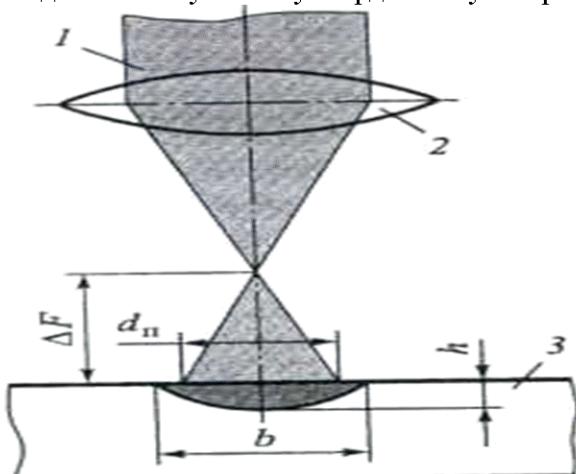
Схема лазерної обробки. 1 – промінь лазера; 2 – лінза; 3 – деталь
